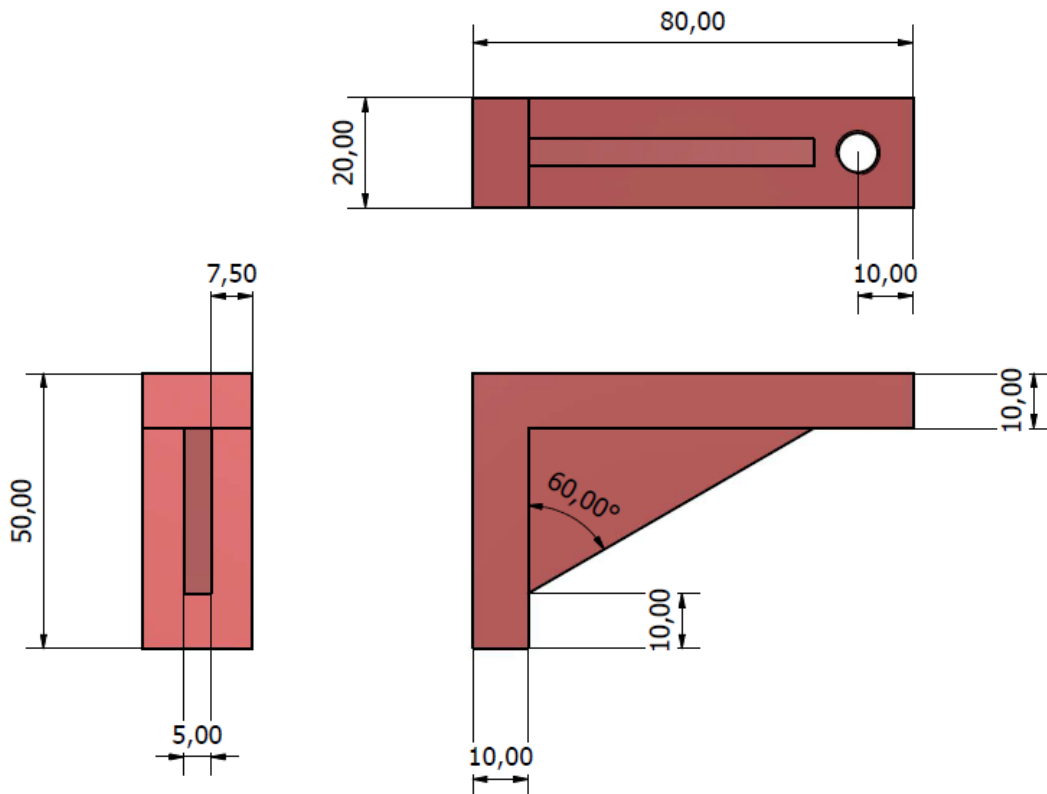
Dimensioni degli elementi che permetterebbero il collegamento tra trave e piattaforma.
